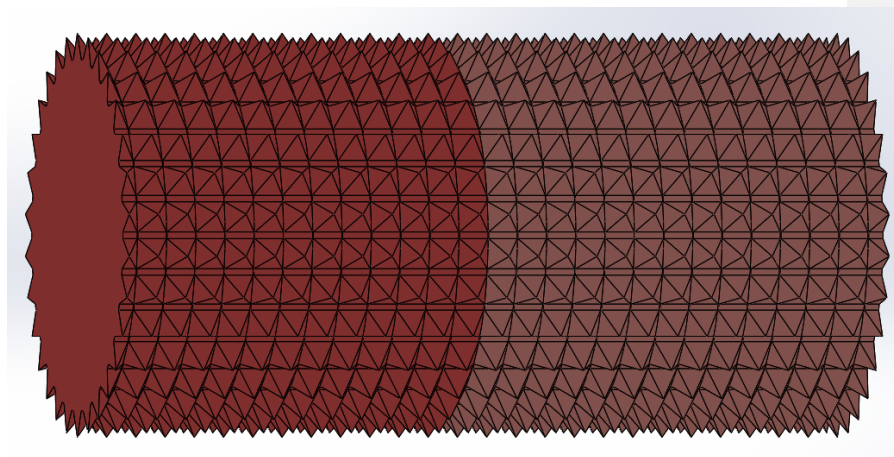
Disposición de soldadura 3º maza superior
